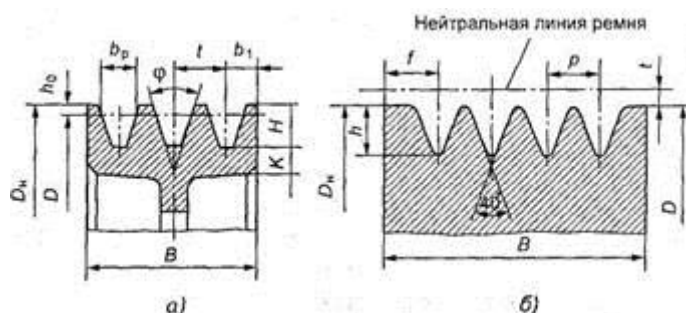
Конструкции шкивов клиновых и поликлиновых передач:
